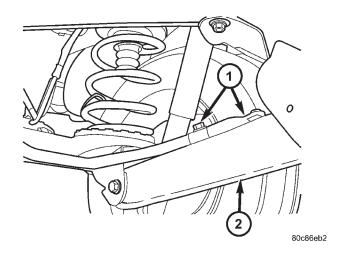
SOPORTES DE LA BARRA ESTABILIZADORA
